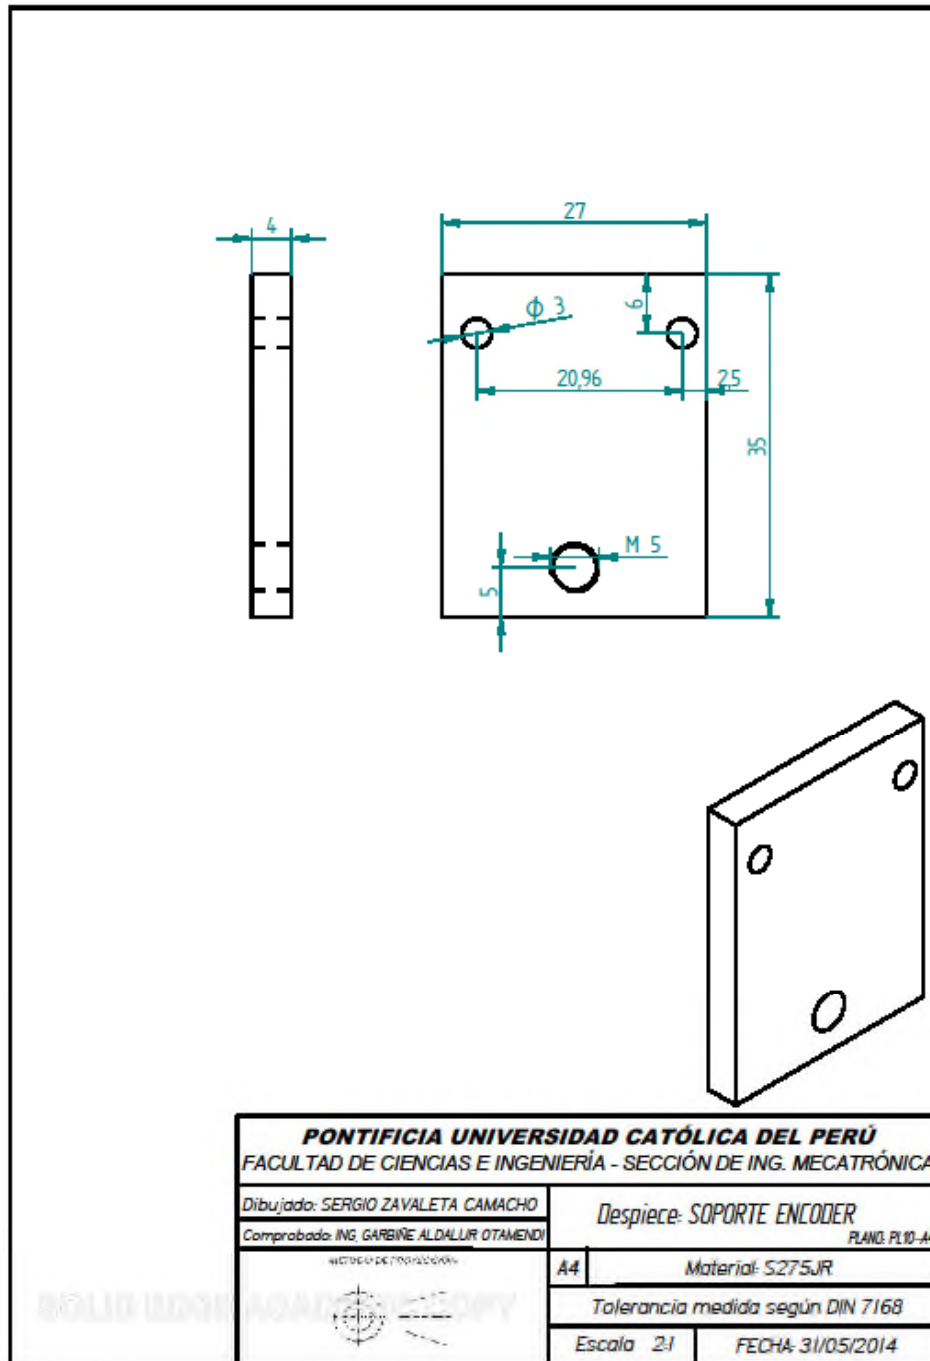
Plano de despiece del soporte del encoder. Fuente: Elaboración propia.
